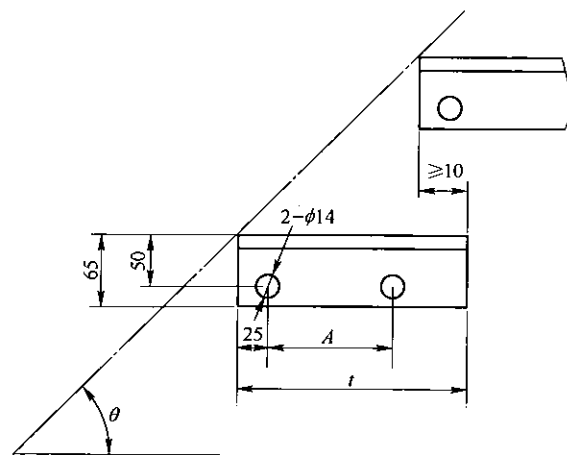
端板尺寸 t 安装孔 A 的尺寸
